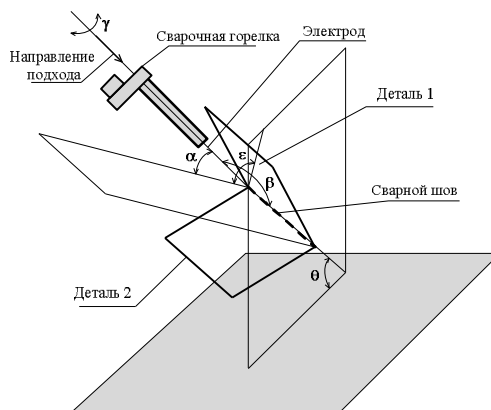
Ориентация горелки дуговой сварки и сварного шва
